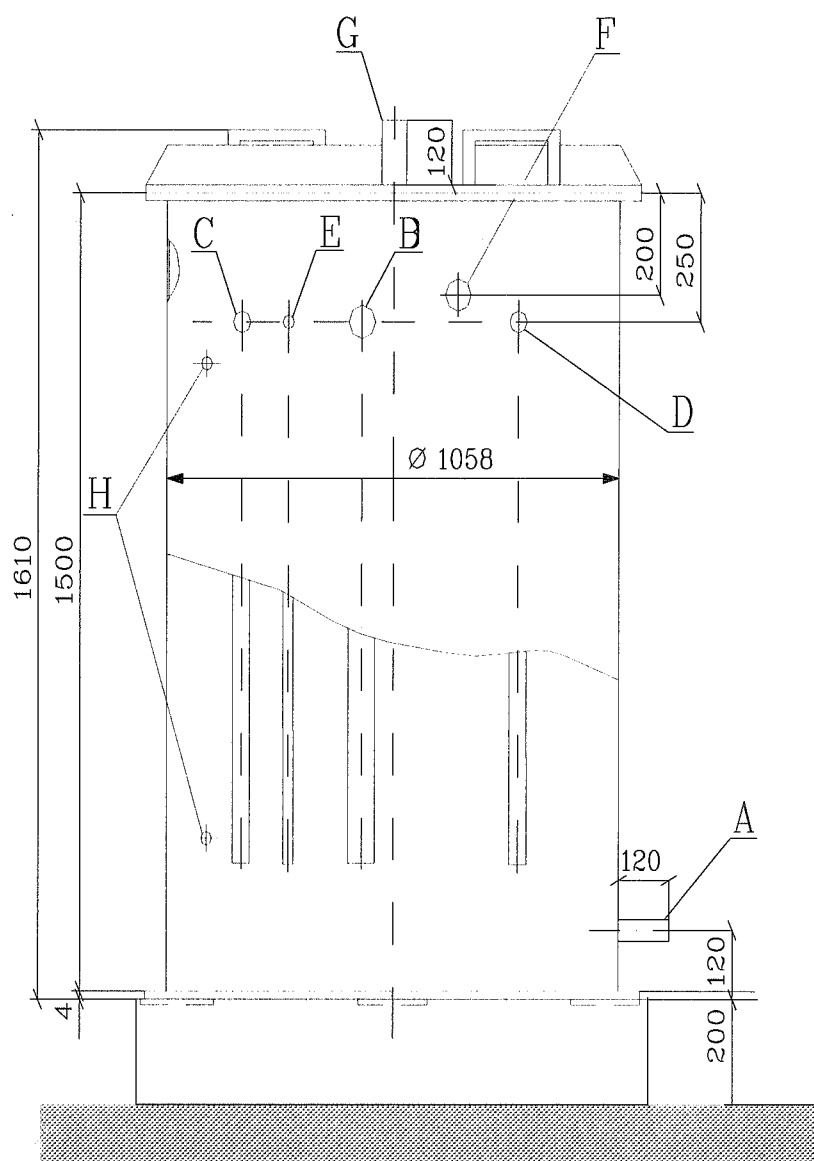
Габаритный чертеж бака сбора стоков содержащих химреагенты
